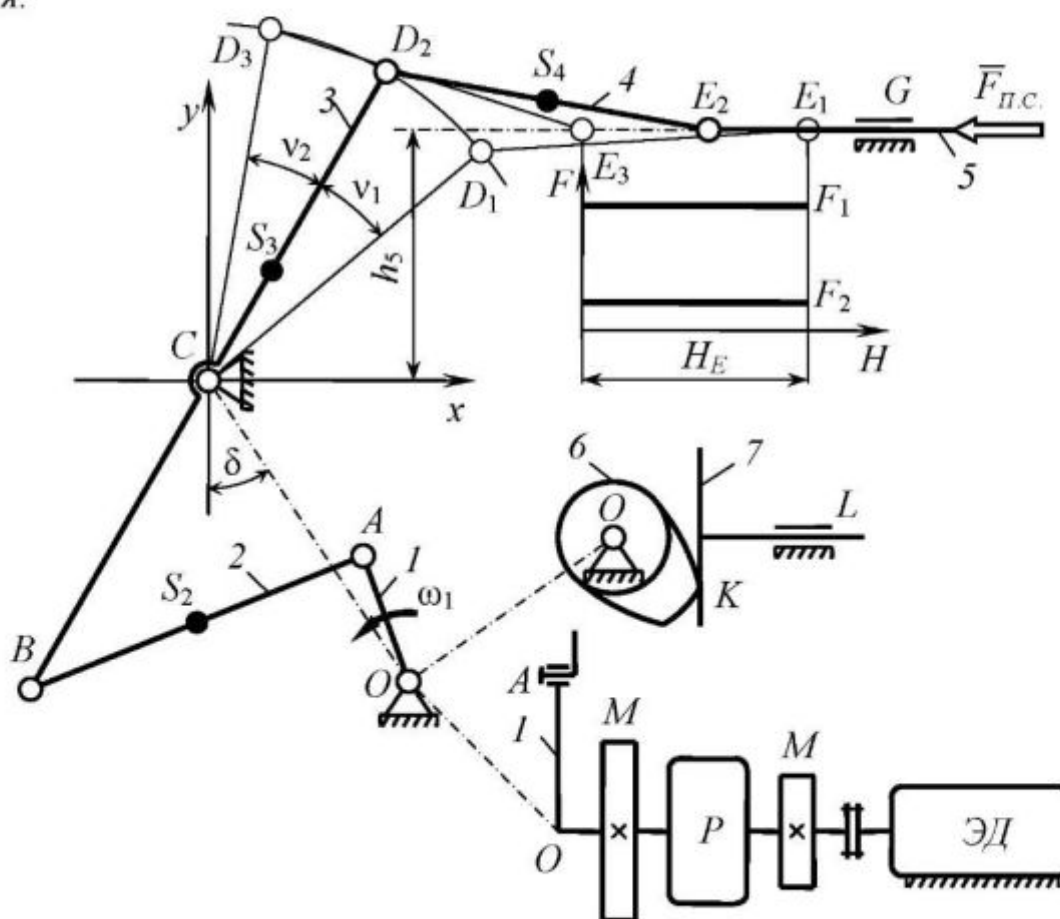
Кинематическая схема механизма подачи деталей на конвейер
